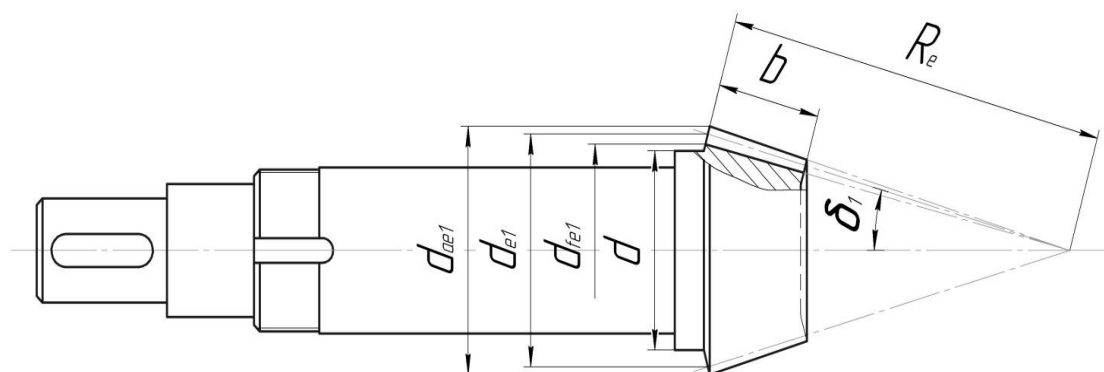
Конструкция вала-шестерни (конической)
